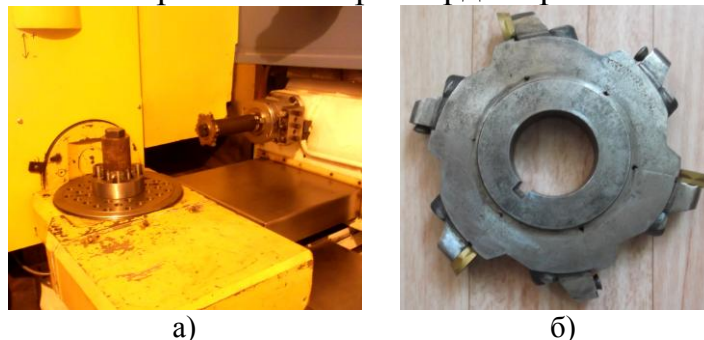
Общий вид наладки станка MC 032 и экспериментальный образец дисковой фрезы с быстросменными пластинками Sandvik Coromant R300-1648M-PH
